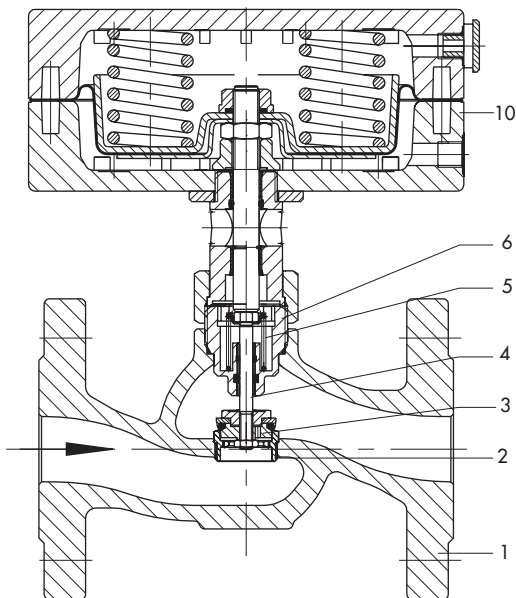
· Пневматический регулирующий клапан типа 3213/1780-1 с проходным клапаном типа 3213 и приводом типа 2780-1
